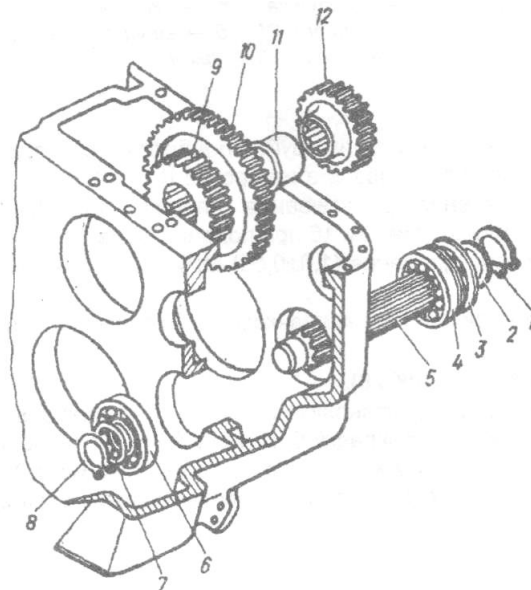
Установка ходозменшувача: 1, 2, 3, 7, 8 — кільце; 4, 6 — підшипник; 5 — вал; 9, 10, 12 — зубчасте колесо; 11 — втулка
